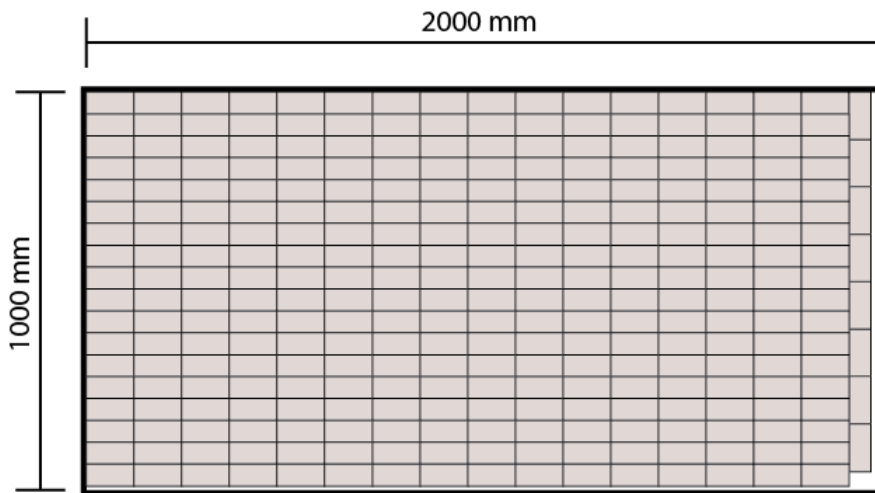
Cortes de las piezas “apoyos de presión” en una plancha de grilon
